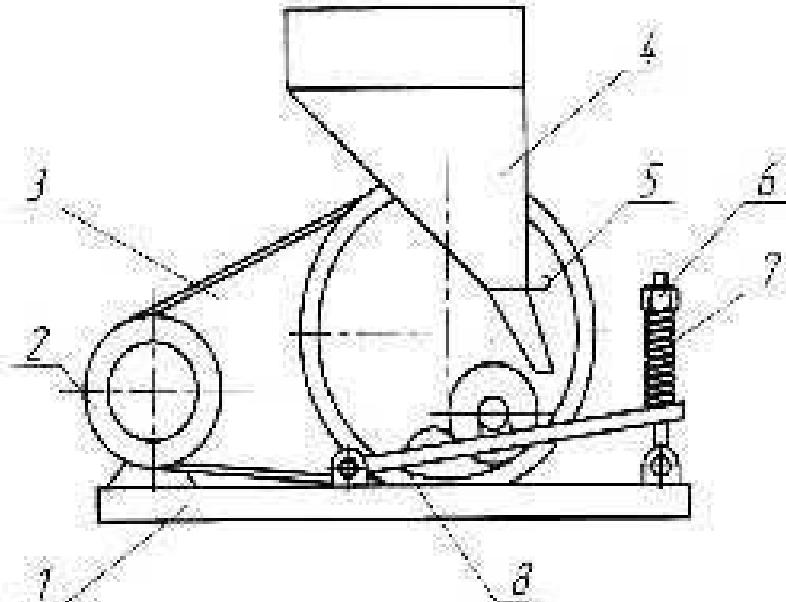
схема миниплющилки зерна по патенту № 52342
